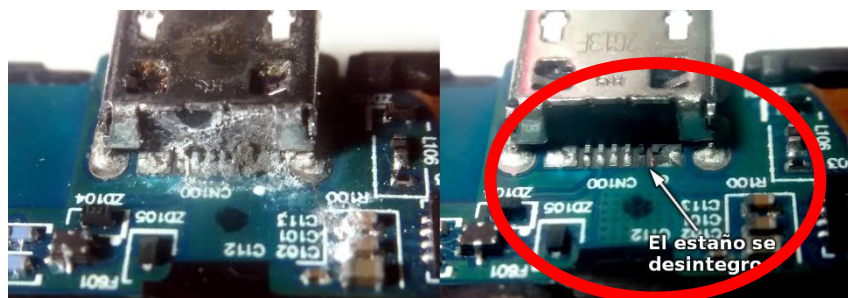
Presencia de sulfato en conector / identificación de pin de soldadura desintegrado luego de la limpieza.
